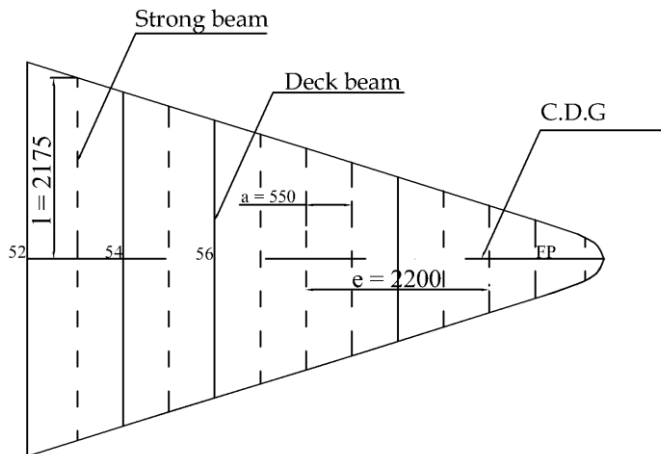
Panjang Tak ditumpu (l) Strong beam Bangunan atas dan rumah geladak
